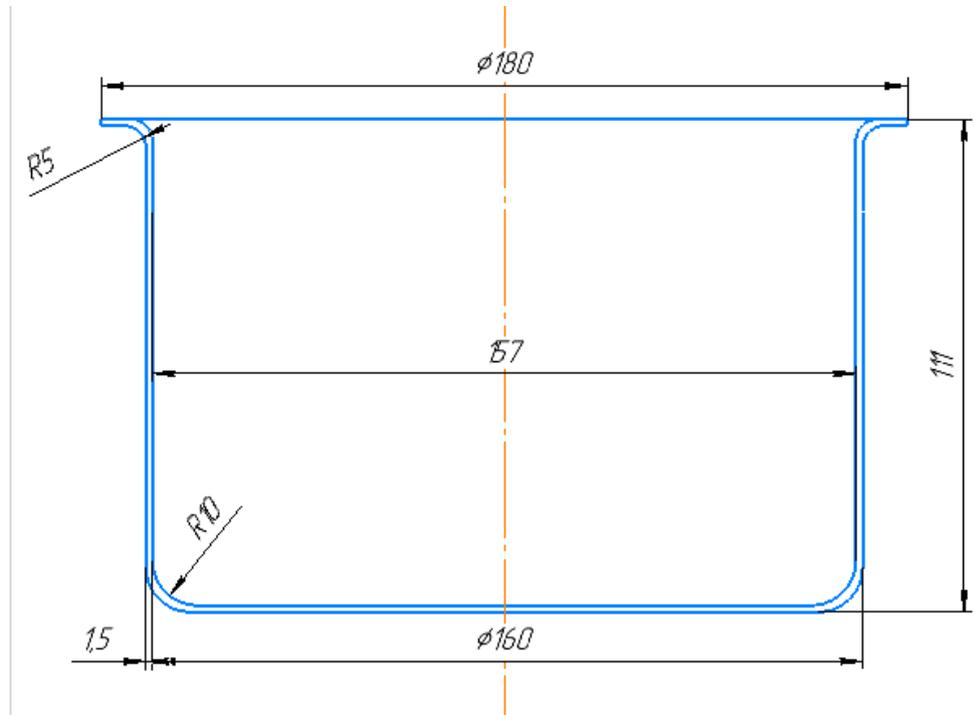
Чертеж детали «Корпус кастрюли»
